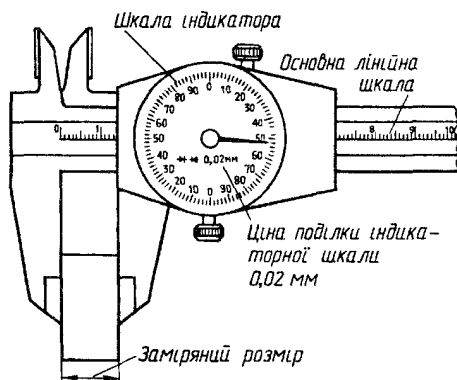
Штангенциркуль з індикатором годинникового типу
